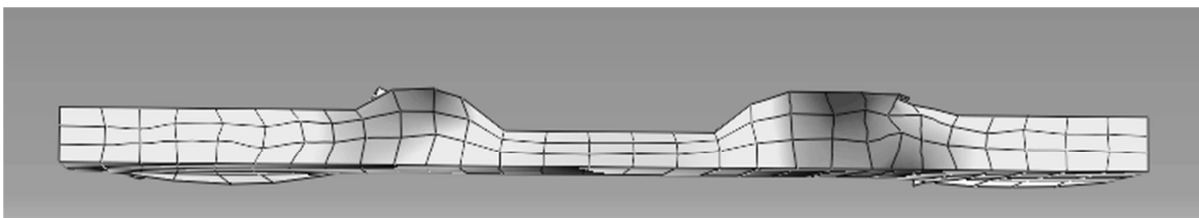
Другий етап моделювання пластичного деформування заготовки з оптимальним об'ємом
